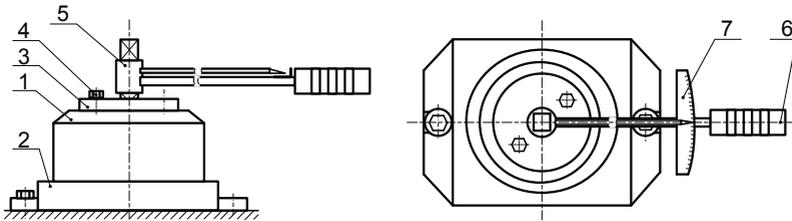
Устройство для проверки угла опережения впрыска топлива: 1- муфта; 2 – плита; 3 – шайба; 4 – винты; 5 – динамометрический ключ; 6 - рукоятка; 7 - шкала
